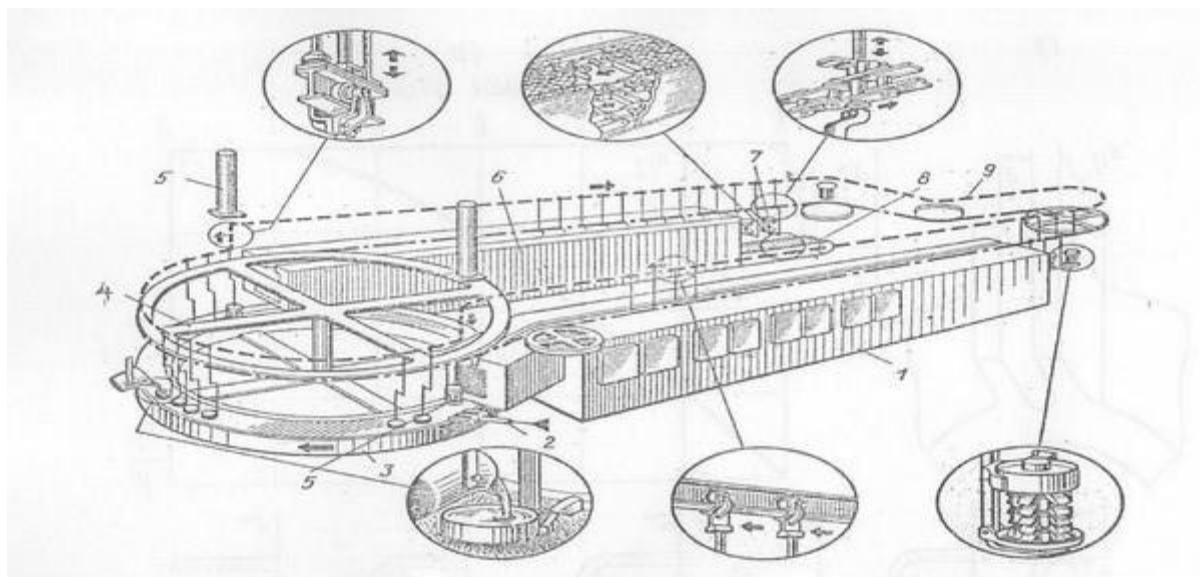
Схема агрегата для прокаливания, формовки, заливки, и выбивки
